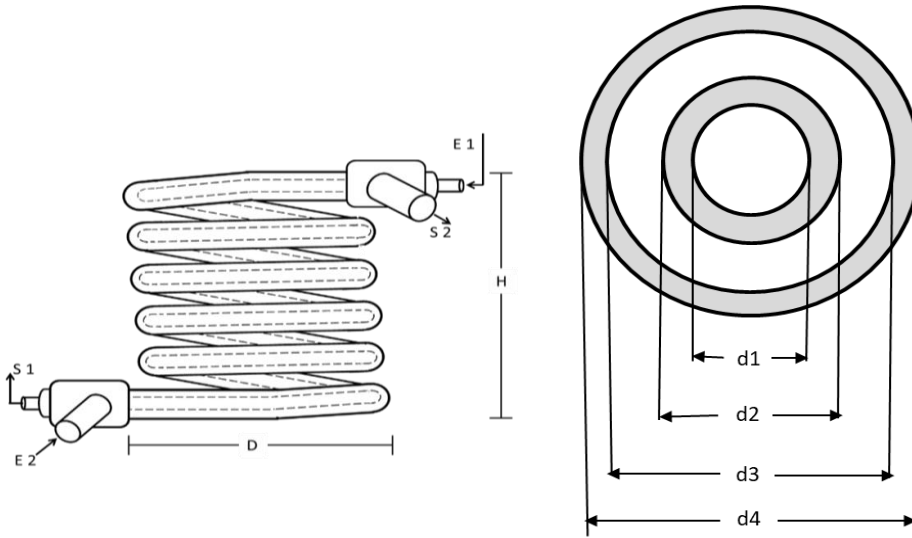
Dimensiones geométricas del evaporador (vista lateral y corte frontal)
